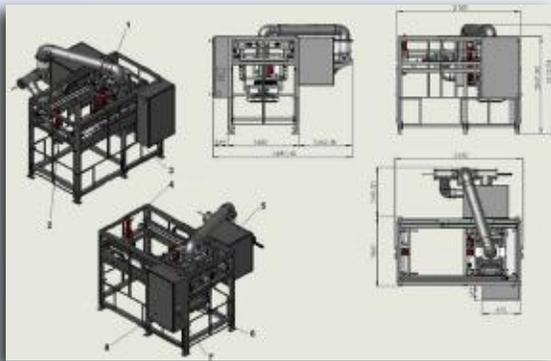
Conjuntos que conforman el desmoldeador de pan.
